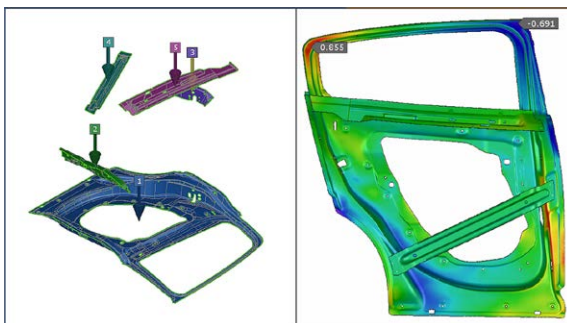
Avaliação de um processo de montagem e solda de peças estampadas, mostrando os resultados dimensionais do conjunto.
